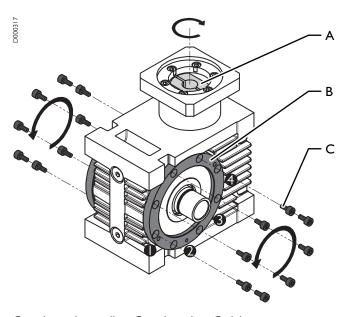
Getriebespiel einstellen: Getriebeeinheit Güdel
